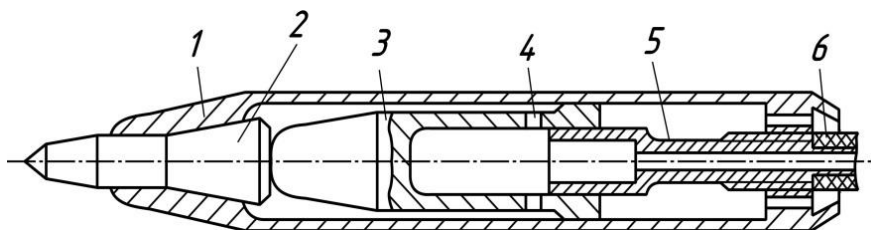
Конструктивна схема пневмопробійника: 1 – корпус; 2 – коваadlo; 3 – ударник; 4 – повітророзподільний пристрій; 5 – клапан; 6 – рукав для стисненого повітря
